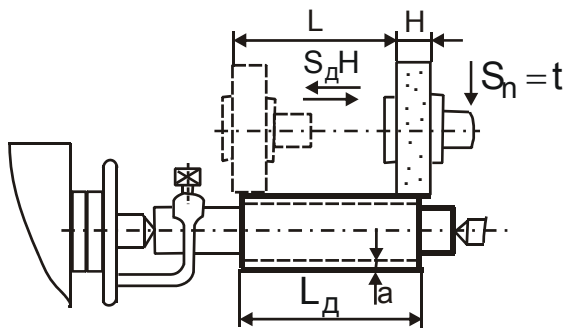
Схема круглого шліфування з поздовжньою подачею
